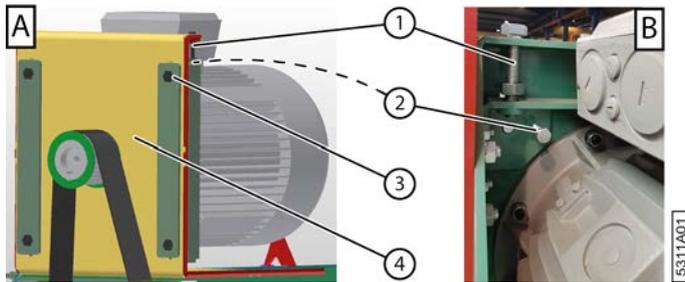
Vue avant [A] et vue arrière détaillée [B] du moteur électrique
